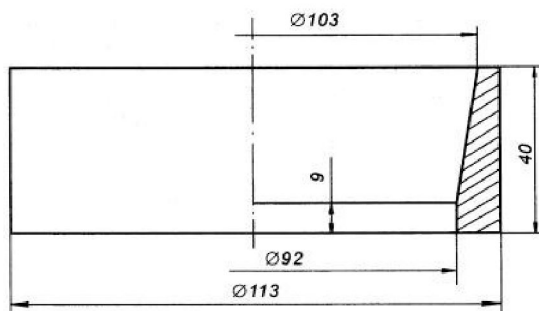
Установка поршня с кольцами в гильзу с помощью оправки.
